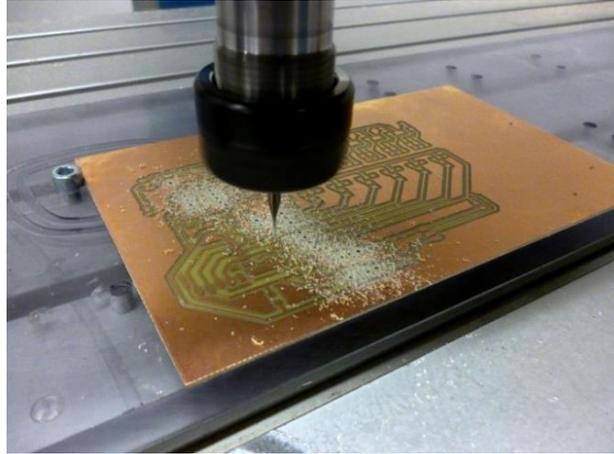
Router CNC para grabado de pistas en placa PCB
